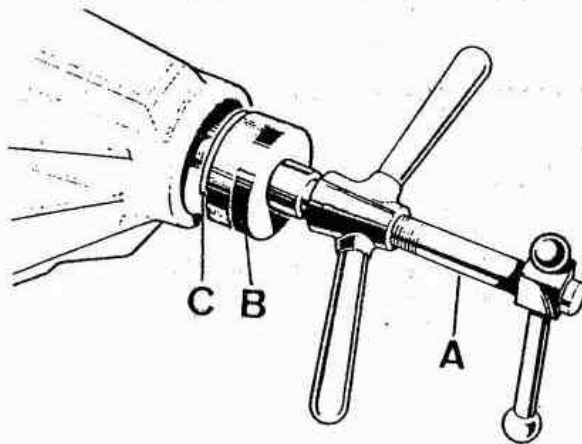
Montaje de la pista del cojinete del extremo de la brida
